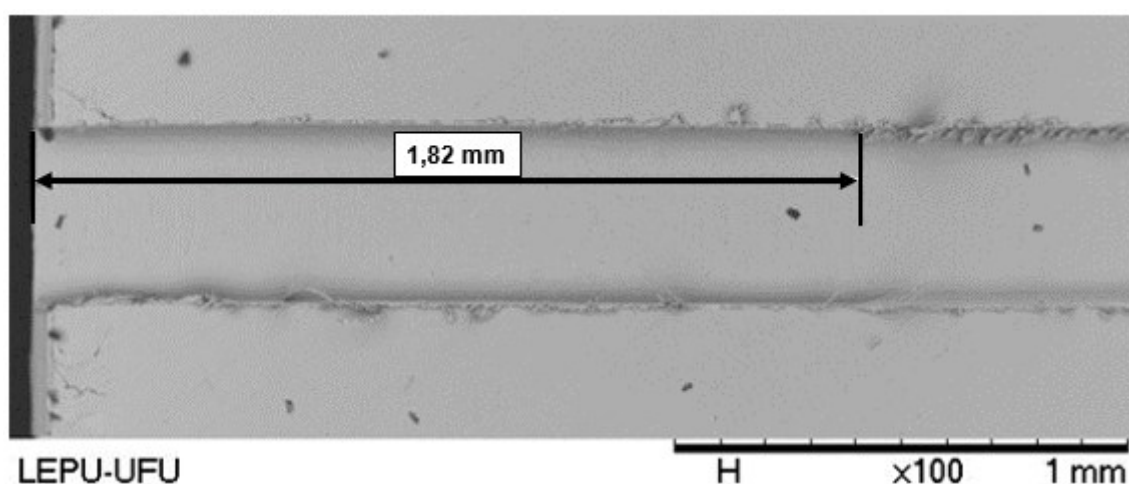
Comprimento de corte usinado antes da quebra da ferramenta
